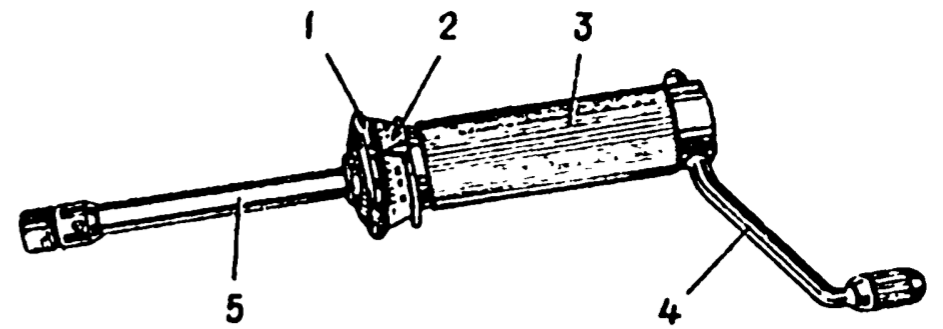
Динамометр 02.7812-9501: 1 - подвижной указатель; 2 - указатель ограничения крутящего момента; 3 - корпус; 4 - рукоятка; 5 - стержень с наконечником, вставляемым в переходную втулку гайки крепления фланца ведущей шестерни
